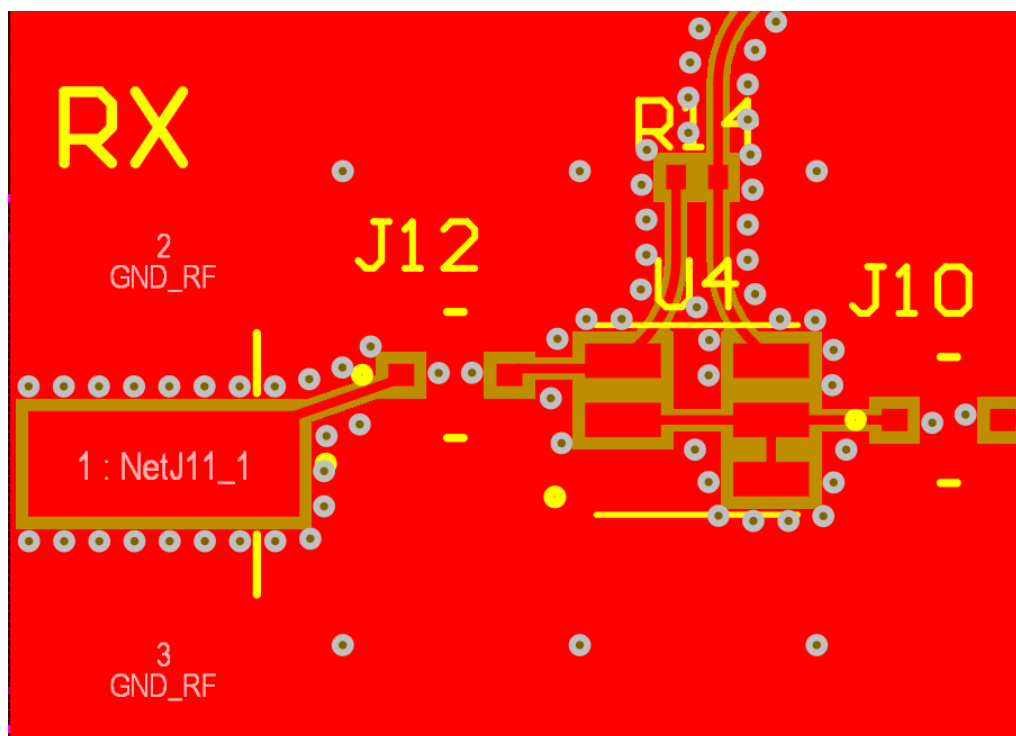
Desenho da entrada RX com combinador em PCB no Altium
